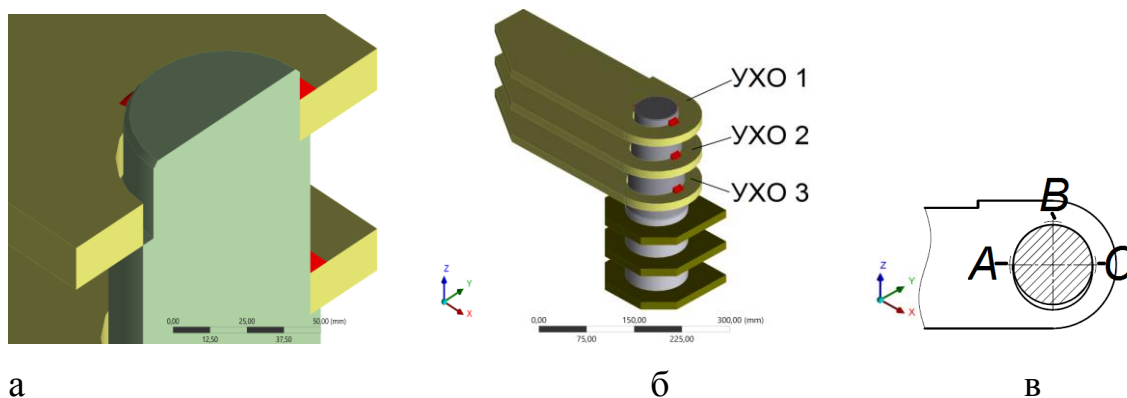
Чертеж сборки петли – ступенчатые петли с зазором и прерывистым сварным швом ((в) – обозначение швов; (б) – обозначение петель, а - плавающая петля со швами в разрезе)
